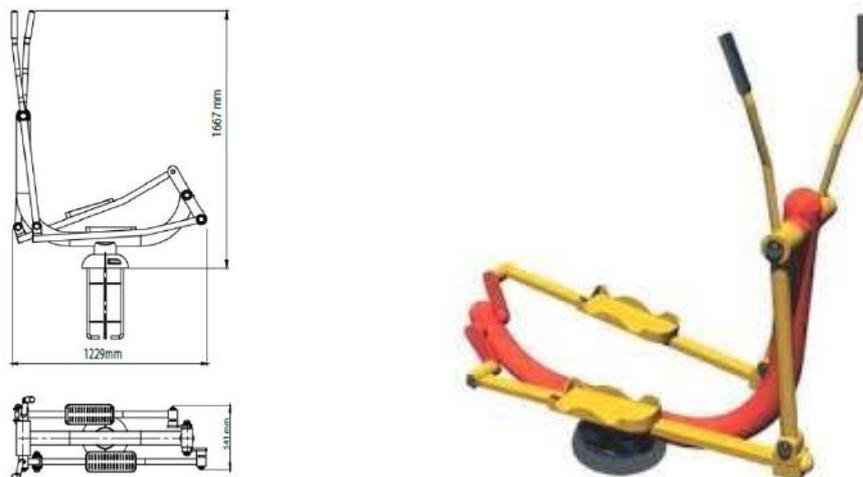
Alzado, perfil y representación 3D esquí
